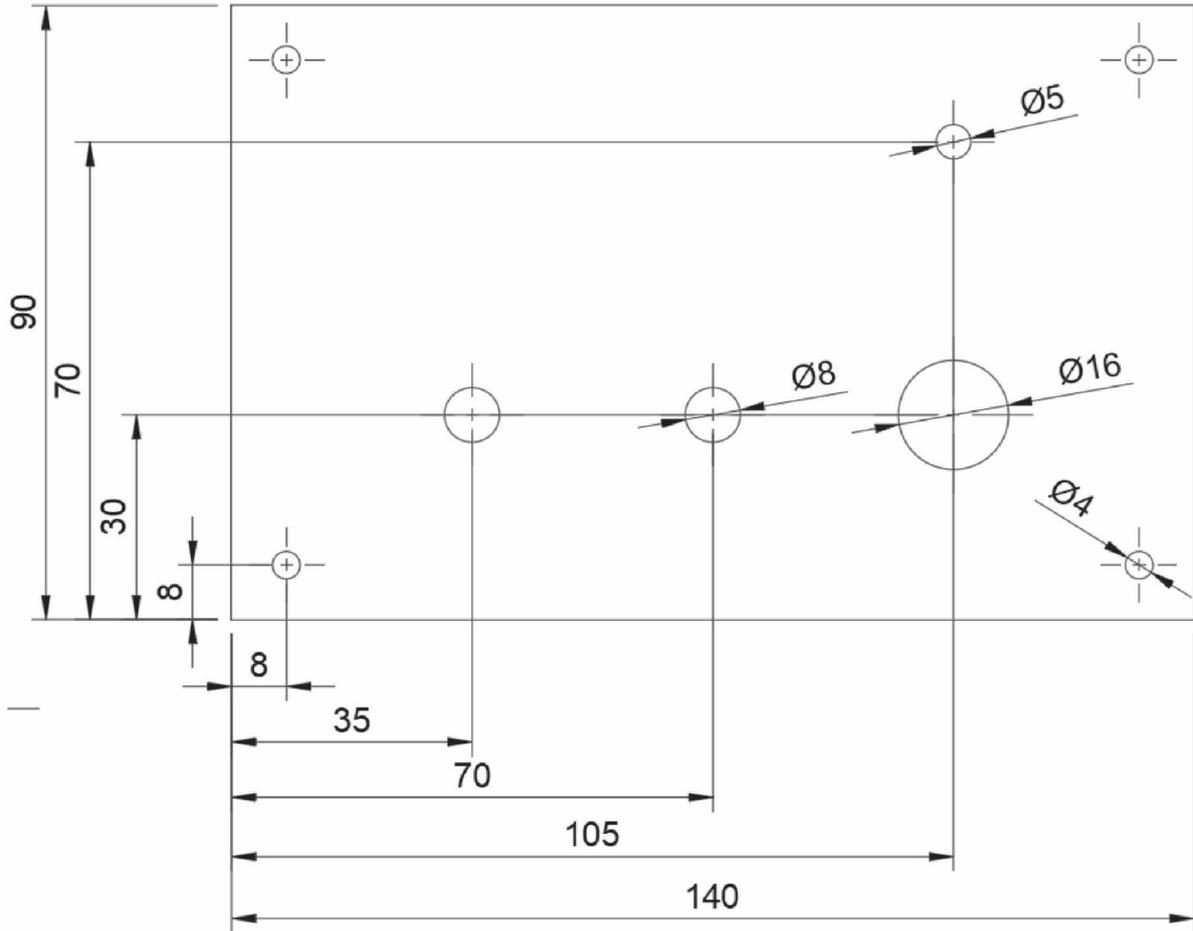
Technische Zeichnung der Aluminiumabdeckung
